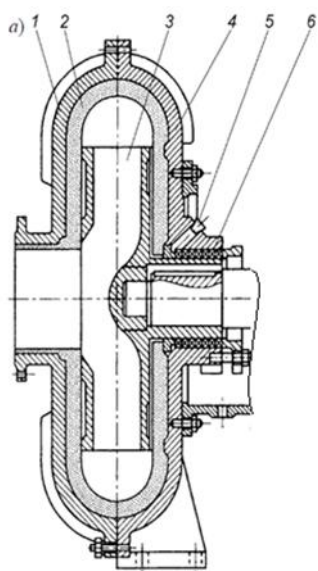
Грунтовий корундо-ваний насос ГрК 1600/50, схематичний розріз (а): 1 - передня половина корпусу; 2 - корундована футерівка; 3 - робоче колесо; 4 - задня половина корпусу; 5 - штуцер подачі віджимної води; 6 - сальник.
